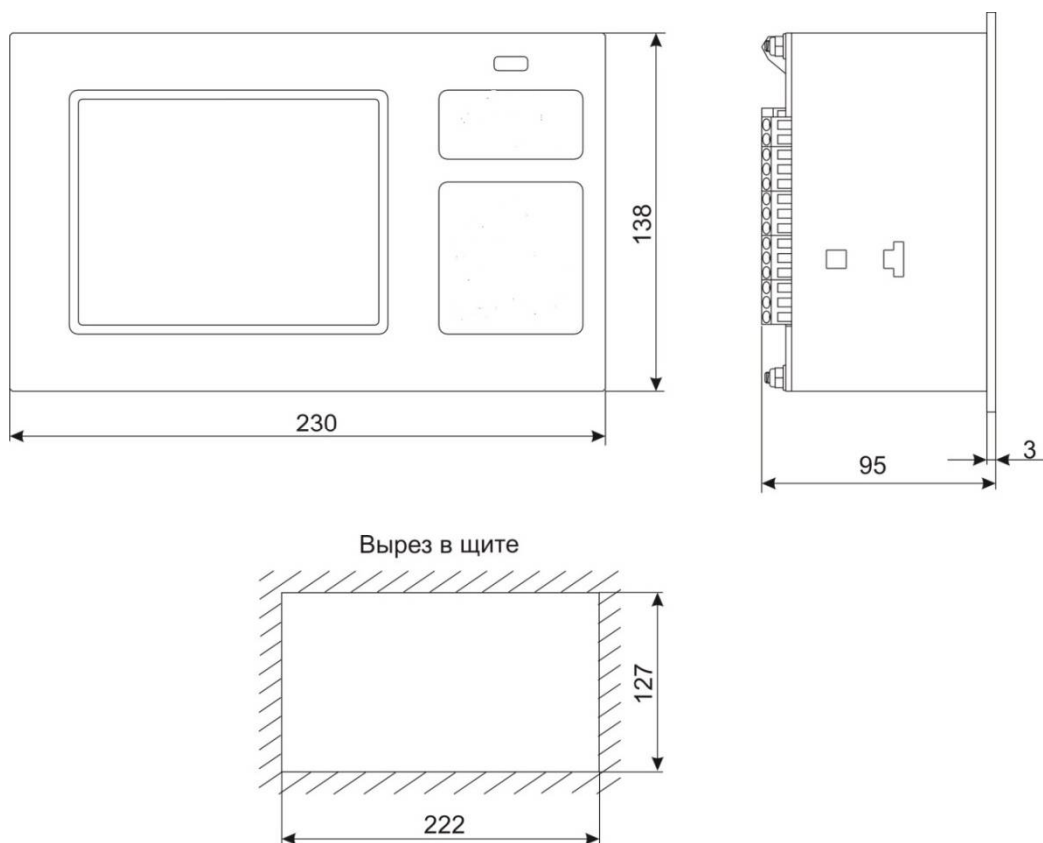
Габаритные размеры основного блока прибора Термодат-29М6/...../F
